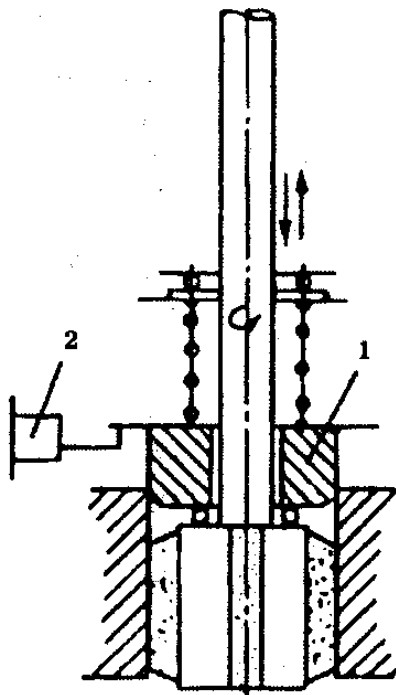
Схема вимірної установки хонінгувального верстату
